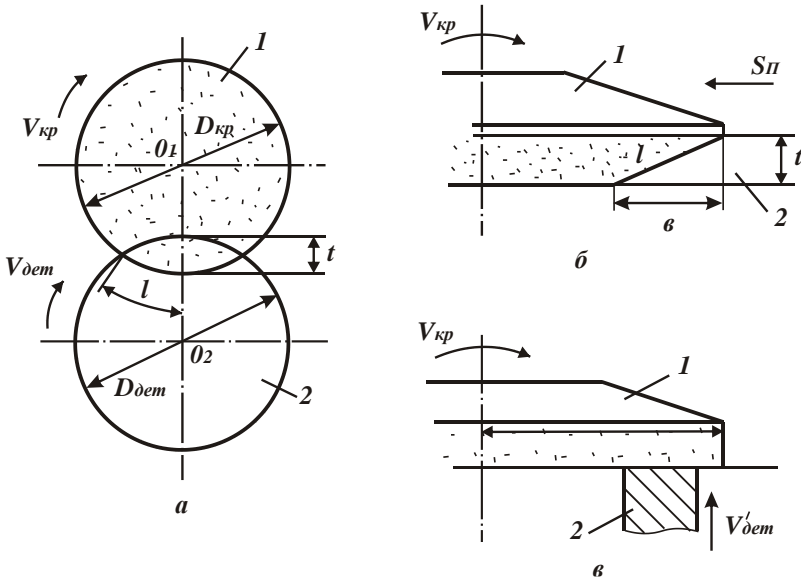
Схеми шліфування: 1 – круг; 2 – деталь
